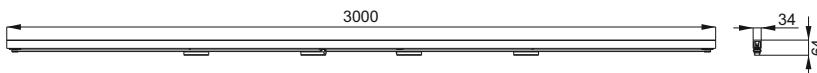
Внешний вид механизма / Figure 1 – Appearance of the mechanism / 1-сурет – Механизмнің сыртқы көрінісі
